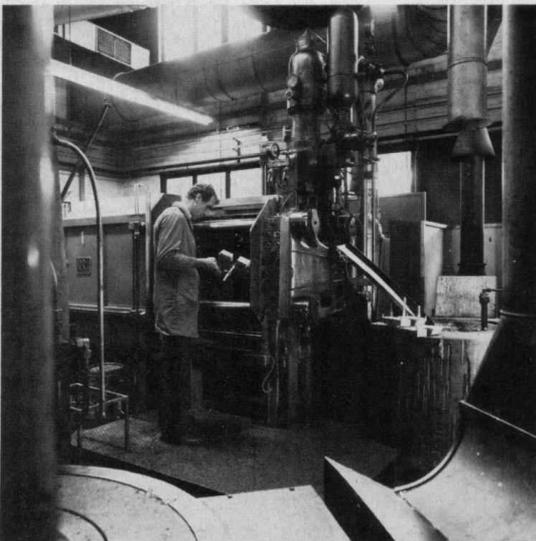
Kaltkammermaschine mit vertikalem Preßkolben
